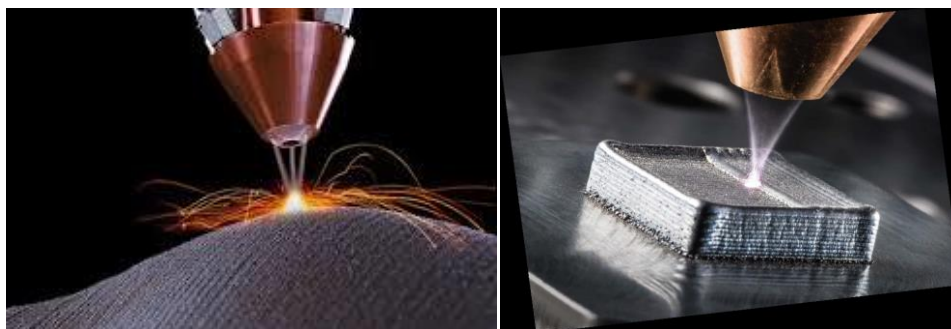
Лазерне наплавлення та легування поверхні заготовки
